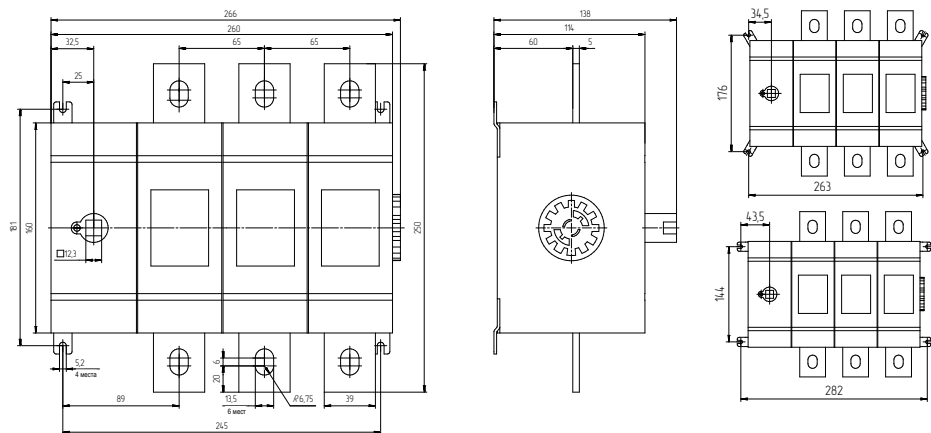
Выключатель-разъединитель 630 – 800 А стандартного исполнения
